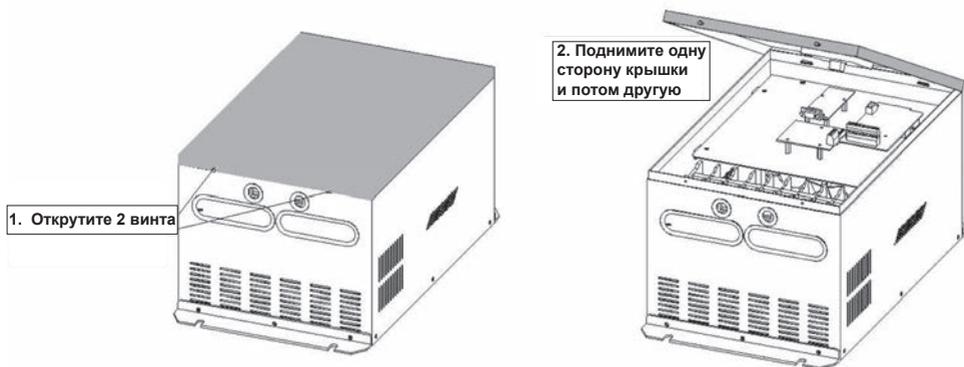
б Демонтаж верхней крышки прибора в металлическом корпусе
